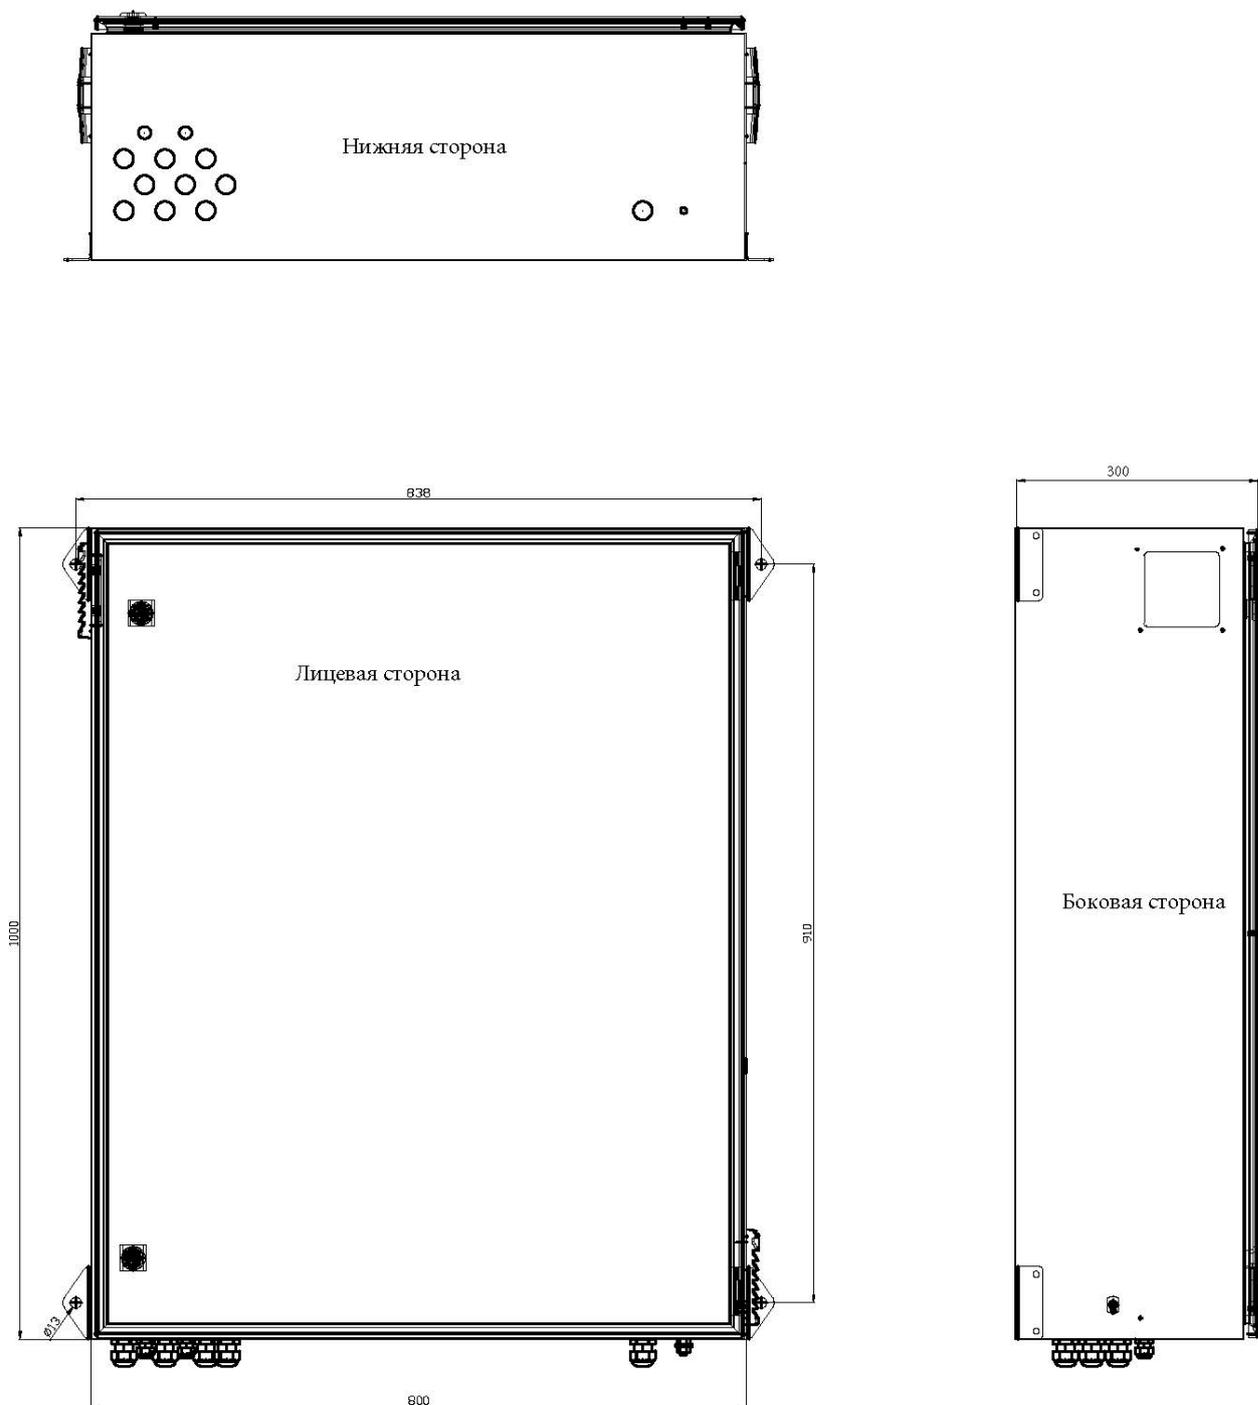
Габаритные размеры шкафа измерительной станции AUX 1 (P100)
